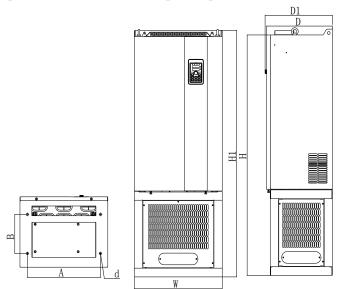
Размер G3 132 ~220 Kw (с основанием реактора постоянного тока)
